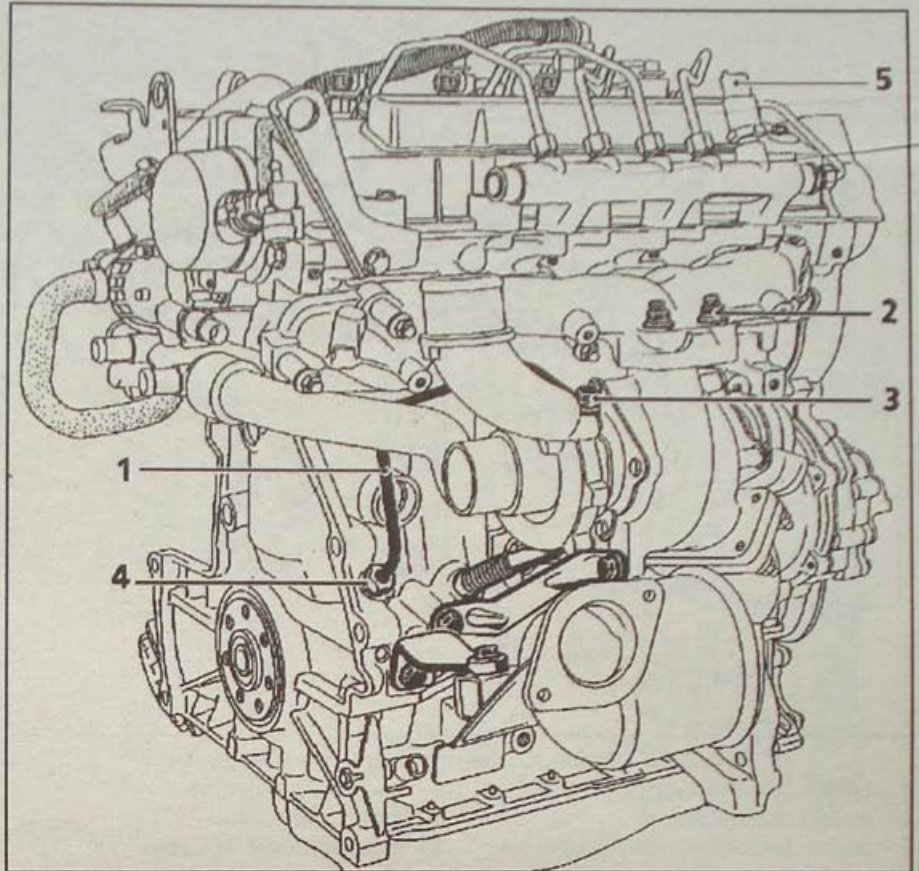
Элементы крепления и подсоединения турбокомпрессора на двигателе G9T:
